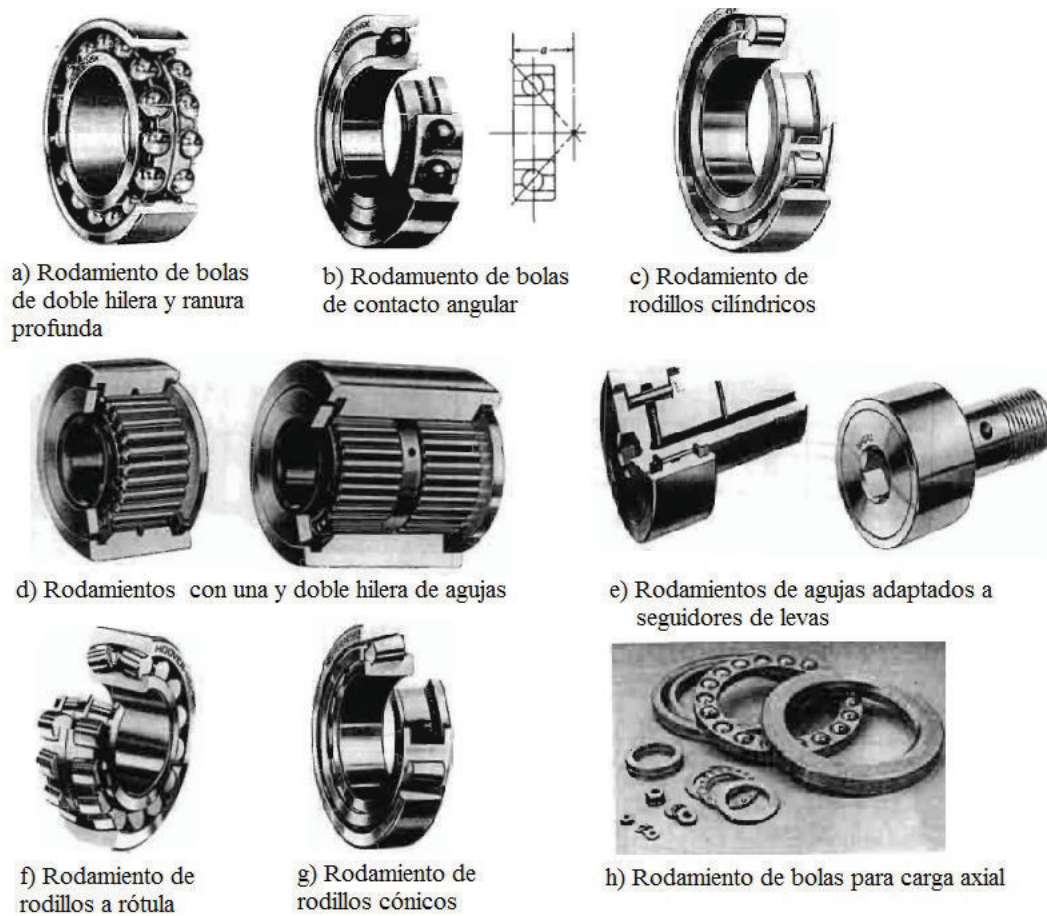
Tipos de rodamientos con contacto de rodadura
